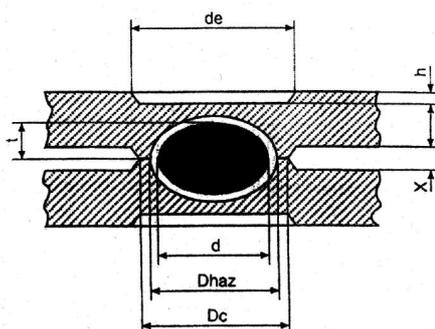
Точечный шов: d_e - диаметр электрода; d - диаметр сварной точки; D_c - пояс пластической деформации; D_{HAZ} - зона термического влияния+сварная точка; h - глубина сварочного следа; t - толщина половины сварной точки.
